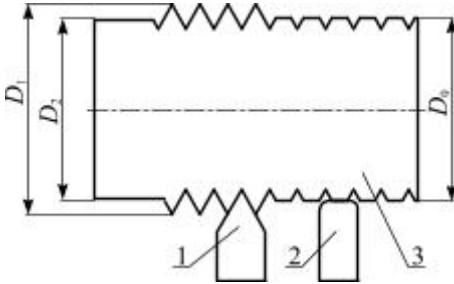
Схема відновлення деталі електромеханічною обробкою: 1, 2 – інструмент для висаджування і згладжування; 3 – деталь; D_2 – діаметр до висаджування; D_1 – діаметр після висаджування; D_0 – діаметр після згладжування
